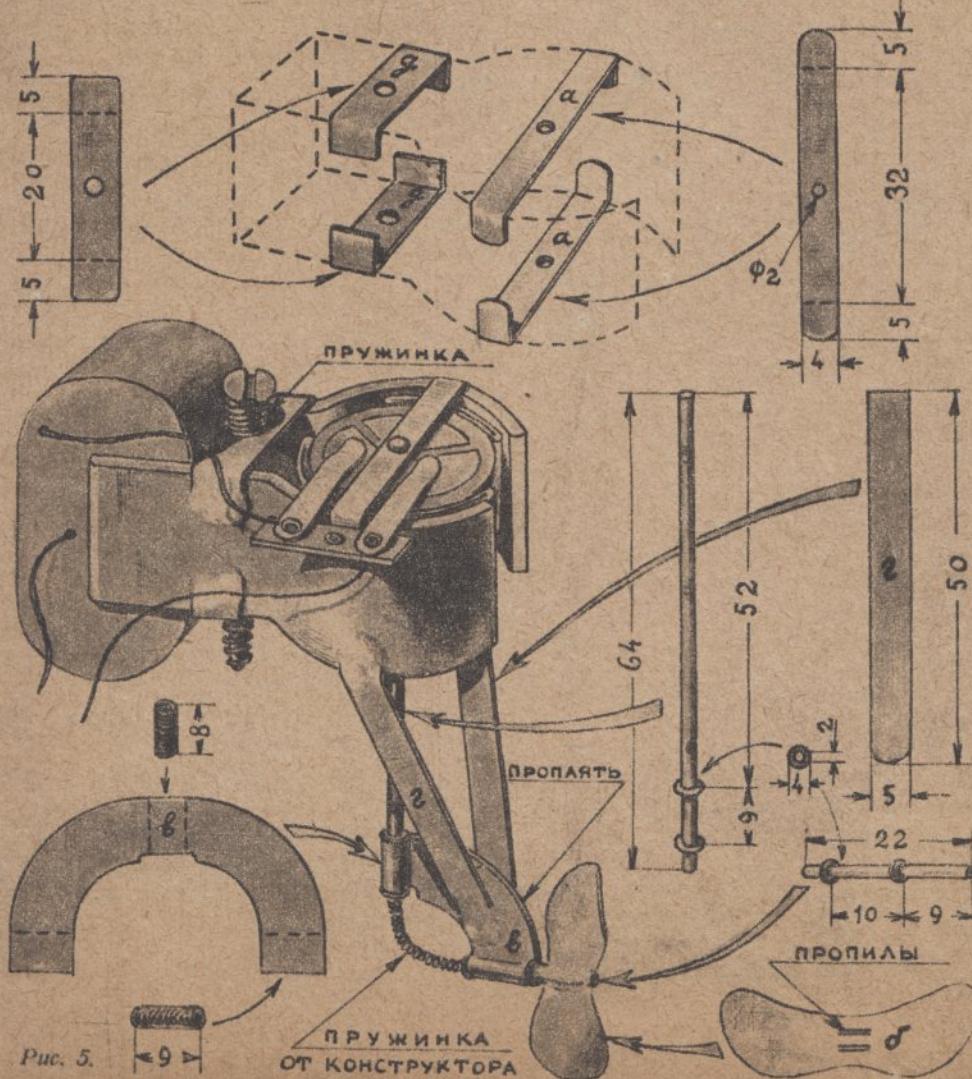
ПРУЖИНКА ОТ КОНСТРУКТОРА
